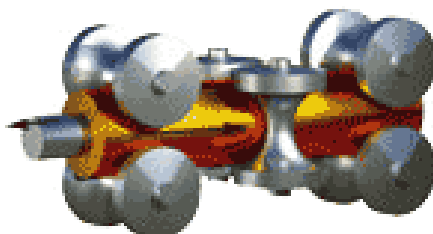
Прокатка на калибровочном стане и извлечение оправки
